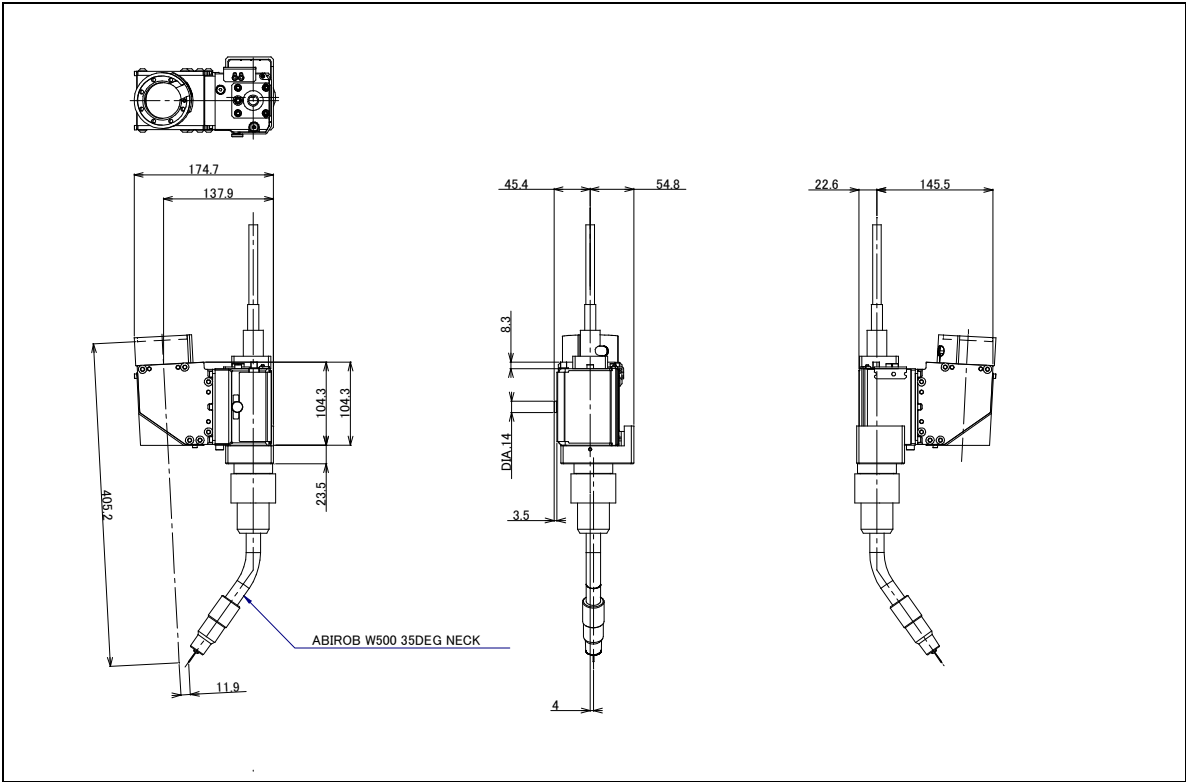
(a) 外形尺寸 (铝用伺服焊炬)
